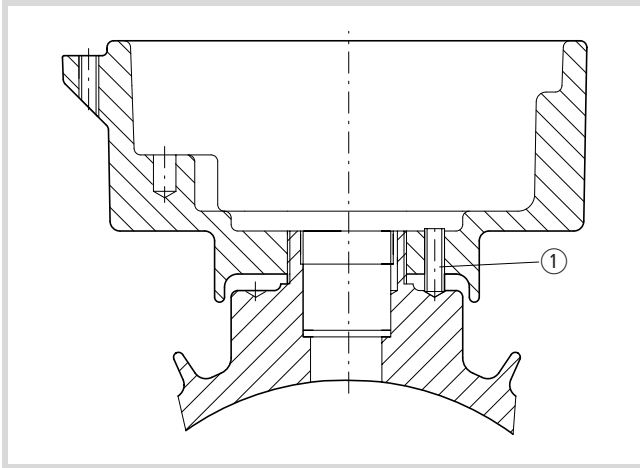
Klemmenkasten (6.01) über Gewinde befestigen
